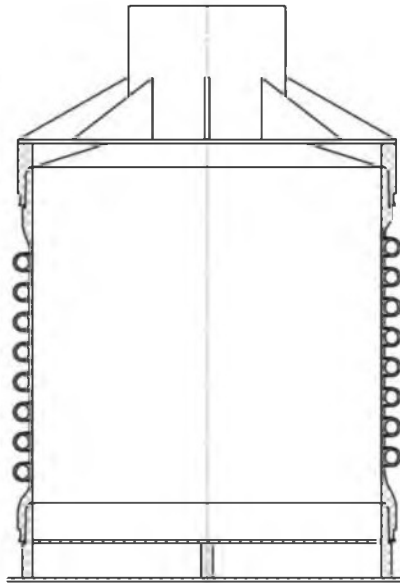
Общий вид специального сборного колодца (после сварки)
